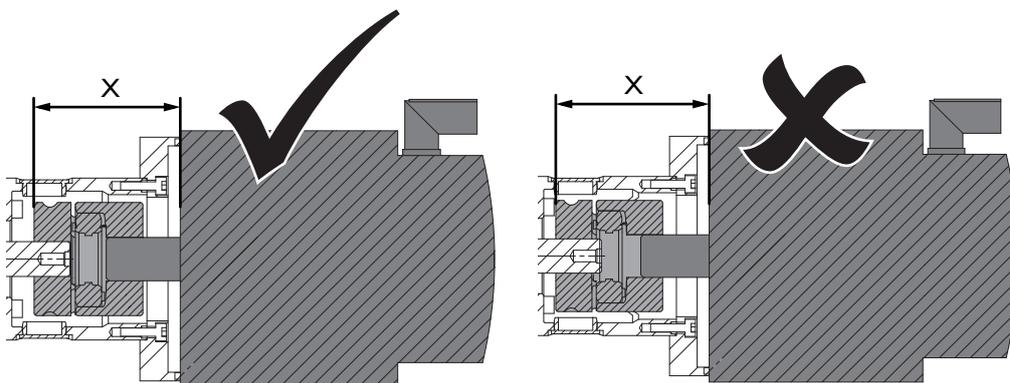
Posizionare il giunto sull'albero motore: sfruttare la tolleranza misura X
